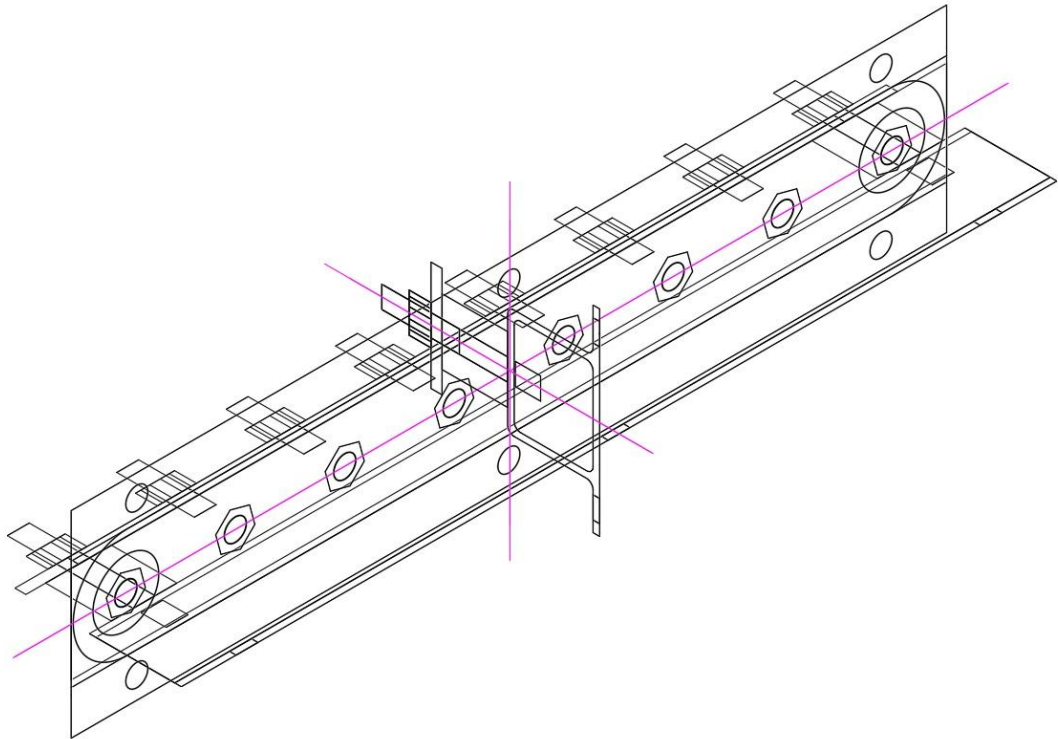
Perspetiva tridimensional da barra de terras em AutoCAD.
